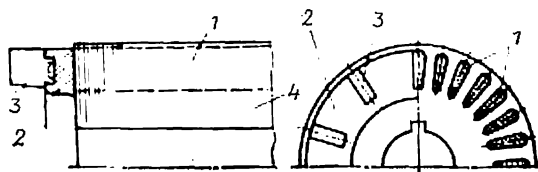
Armature du rotor d'un moteur asynchrone à enroulement en court-circuit coulé en aluminium.
